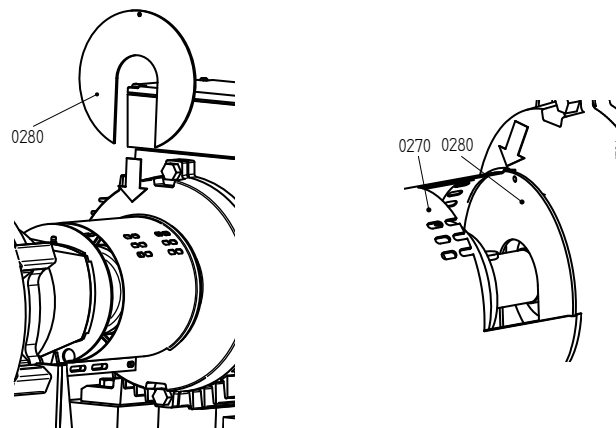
Montieren der Montageplatte auf der Motorseite.
